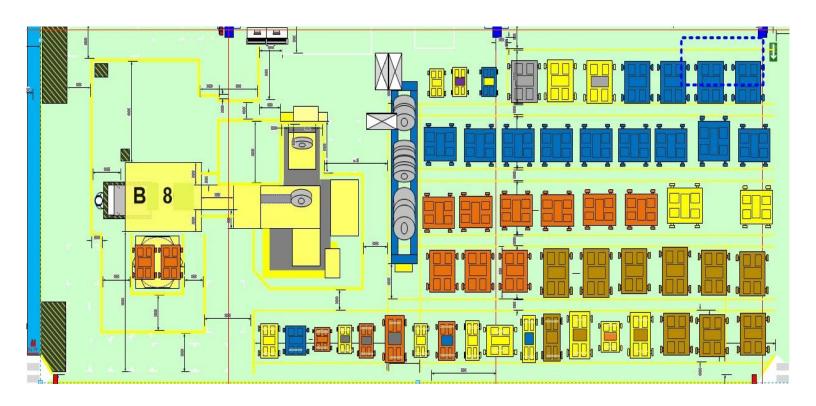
Layout de Prensa Blankin 800 (actual)
